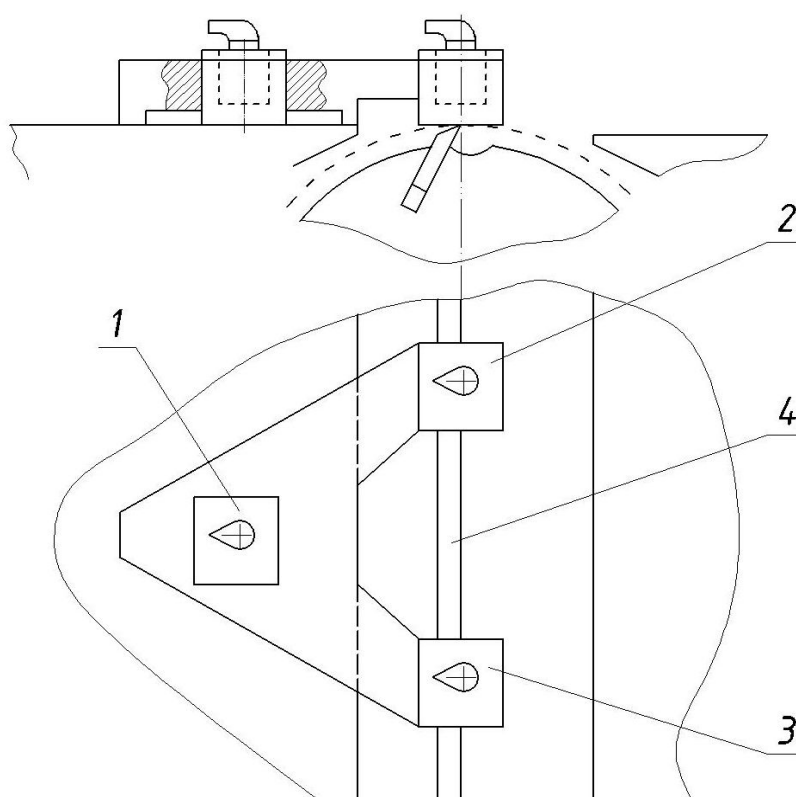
Устройство для установки ножей в ножевом валу фуговального станка
